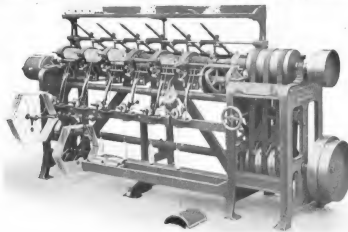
Kreuzspulmaschine für Spulen mit geschlossener Windung.
